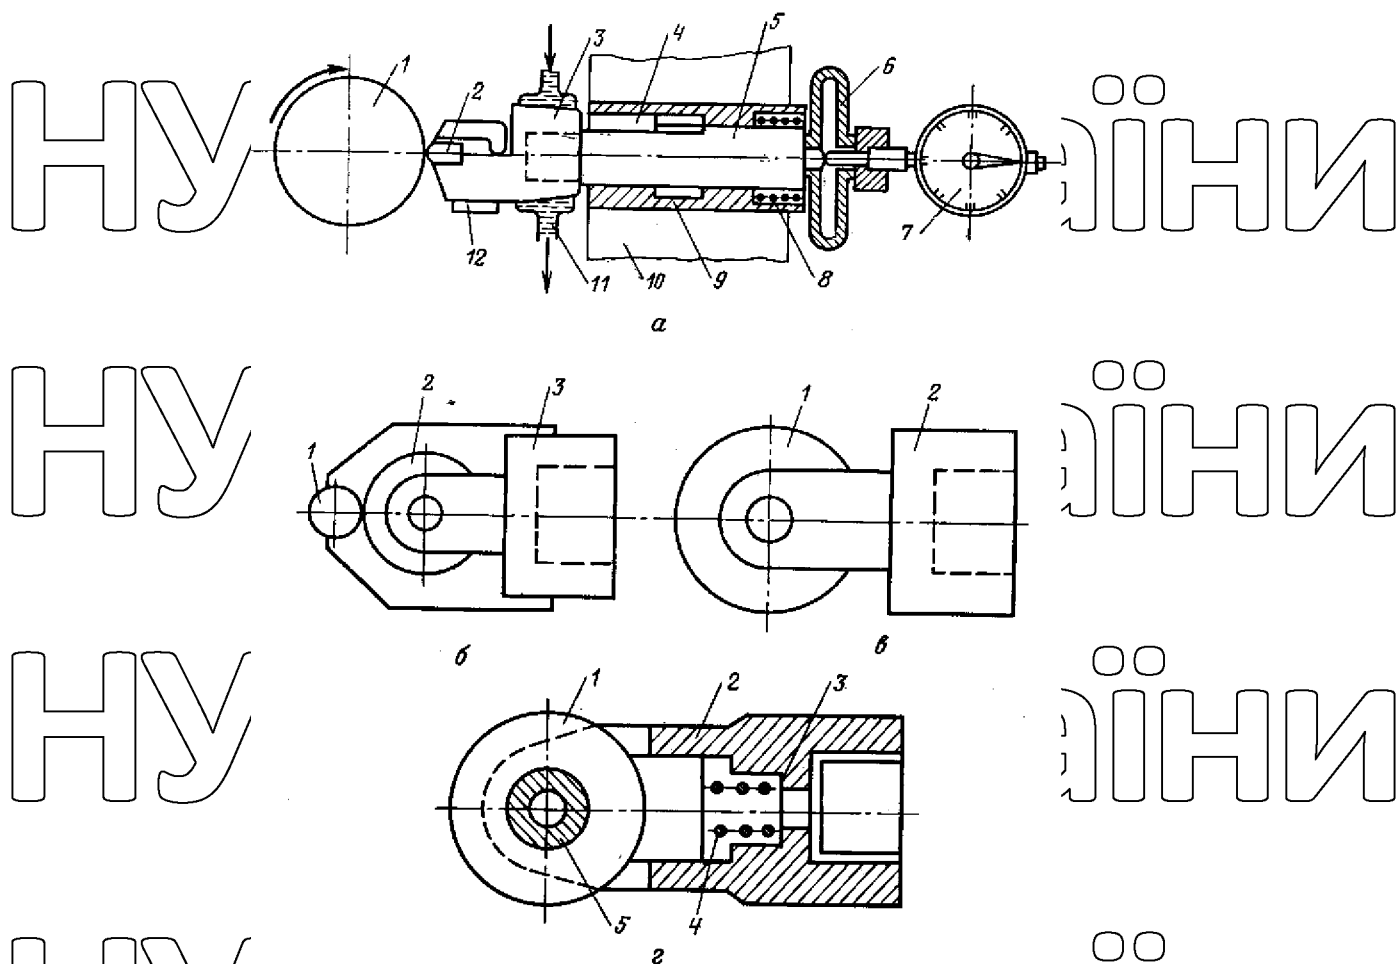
Схема динамометричної оправки (а) зі змінними головками (б, в і г) для зміцнення ЕМО та ППД деталей, відновлених металопокриттями: а-оправлення: 1- деталь; 2 - інструмент; 3 - головка для інструменту; 4 - шпонка; 5 - шток; 6 пружний елемент; 7 - індикатор; 8 - пружина; 9 - втулка корпусу; 10 - єунорт верстата; 11 - охолоджуючий кожух; 12 - наконечник струмопроводу; б - кулькова головка: 1 - кулька; 2 - кульковий підшипник; 3 - вилка головки; в і г - роликіві головки: 1 - ролик; 2 -вилка головки; 3 - мідно-графітова щітка; 4 - пружина; 5-вісь ролика
